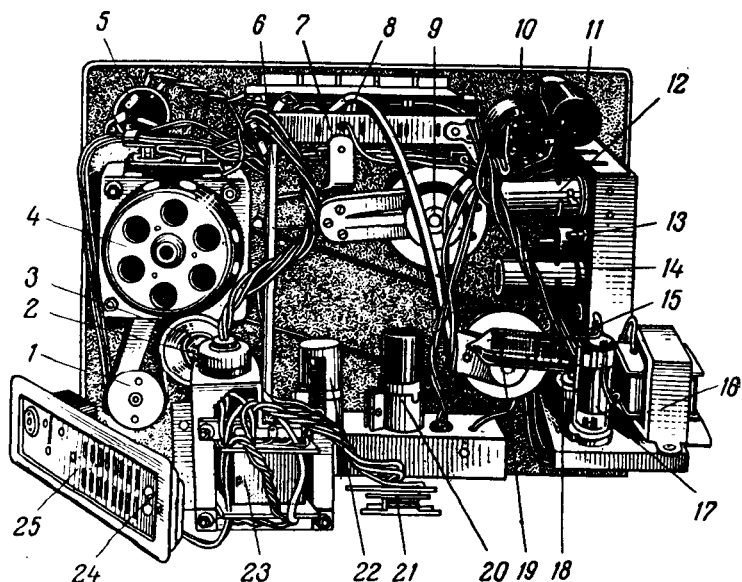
Расположение деталей лентопротяжного механизма и усилителя.
